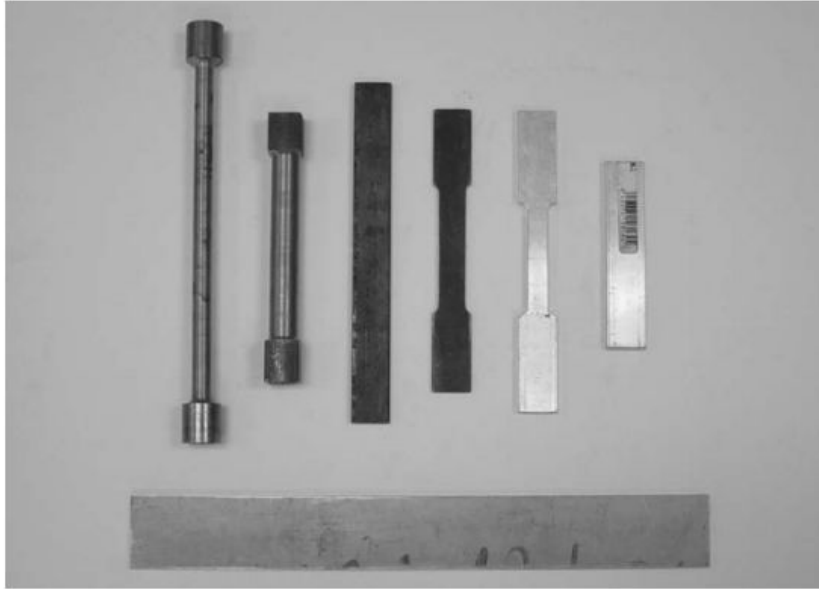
Probetas de ensayo redondeadas y de tipo placa para las pruebas de tracción del acero y el aluminio.
